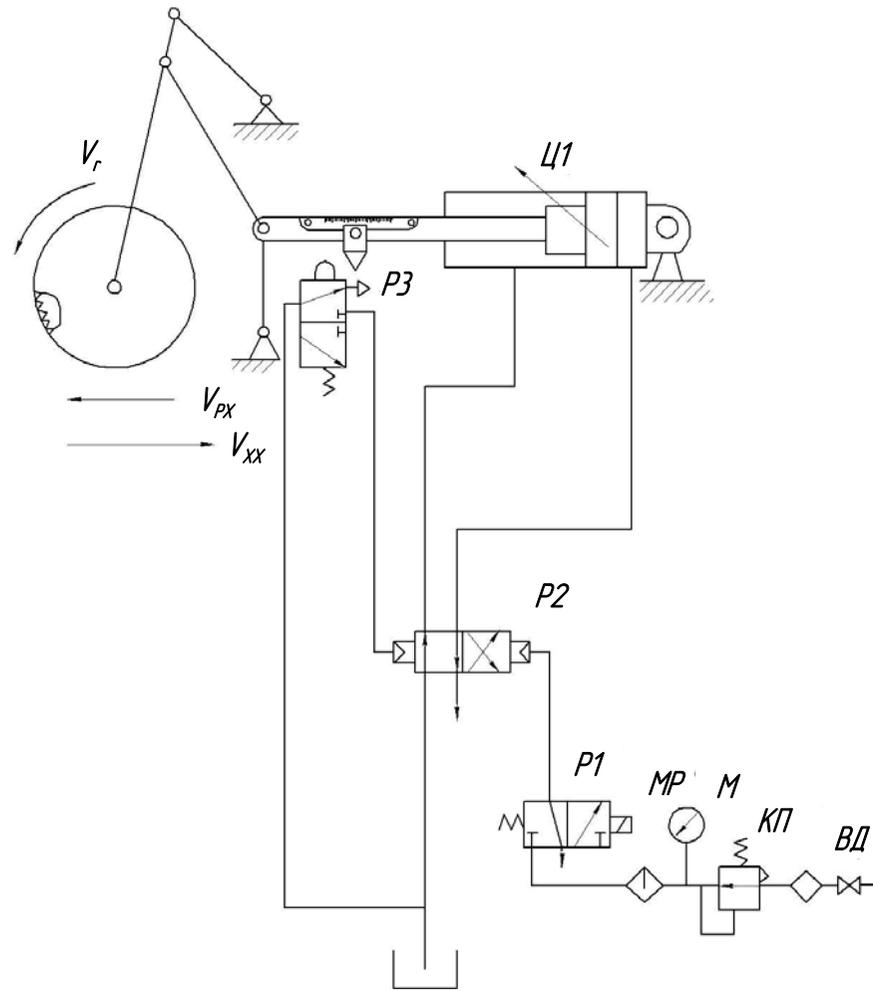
Гидравлическая схема торцовочного станка ЦМЭ-3
